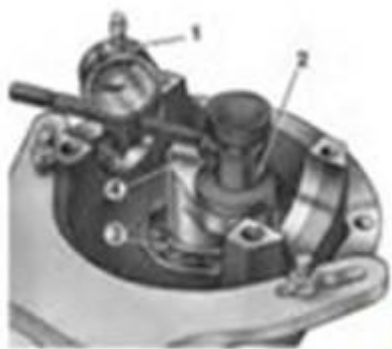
Определение толщины регулировочного кольца ведущей
